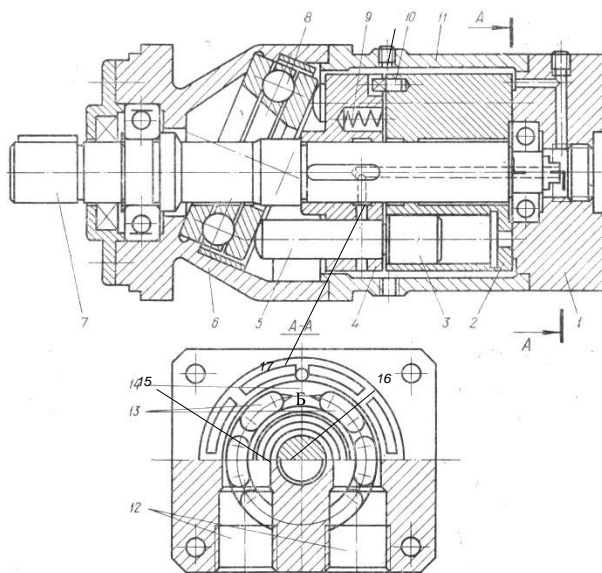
Конструктивная схема аксиально-поршневого гидромотора
